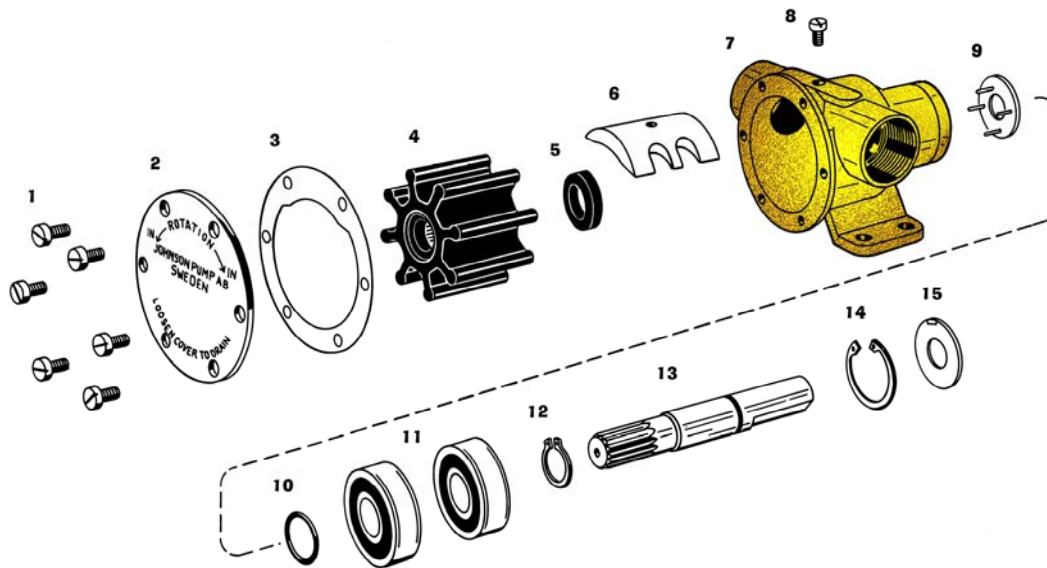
Principen för en flexibel impellerpump (Johnson Pump AB 2005).
